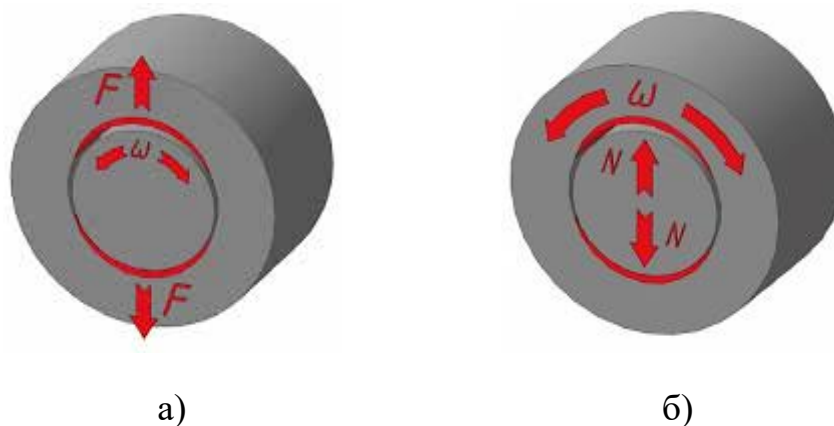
Контактна взаємодія рухомих деталей з'єднань у процесі експлуатації: а) – дія робочої поверхні отвору на зовнішню частину вала; б) – дія зовнішньої частини вала на робочу поверхню отвору
